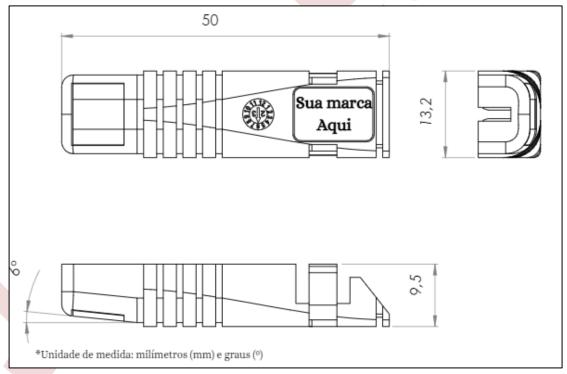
DIMENSIONAL PROTETOR PARA INSTALAÇÃO ATIVA
